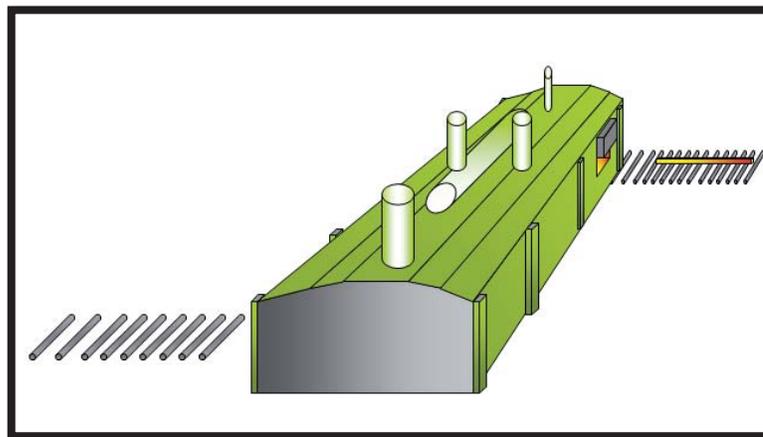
Horno de recalentamiento Planta Colina, Planta Renca.
